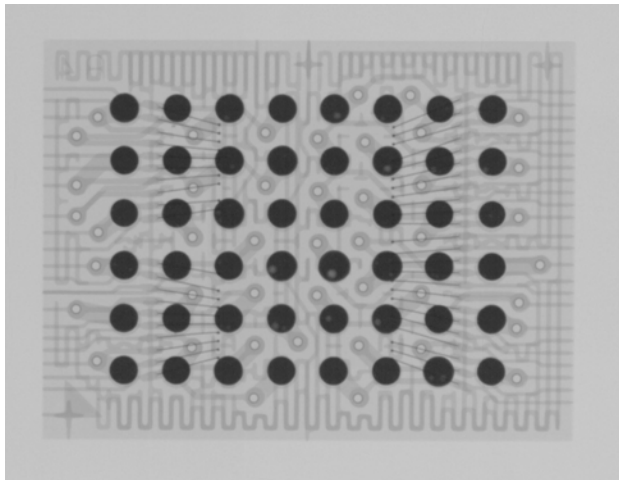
Radiografía del chip BGA-48, soldado en la placa de pruebas.
